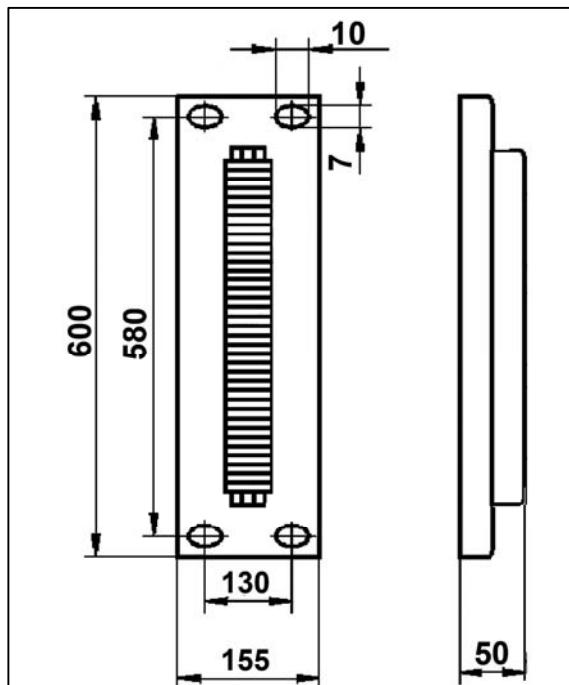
Габаритные и установочные размеры блока БК-1-У3
